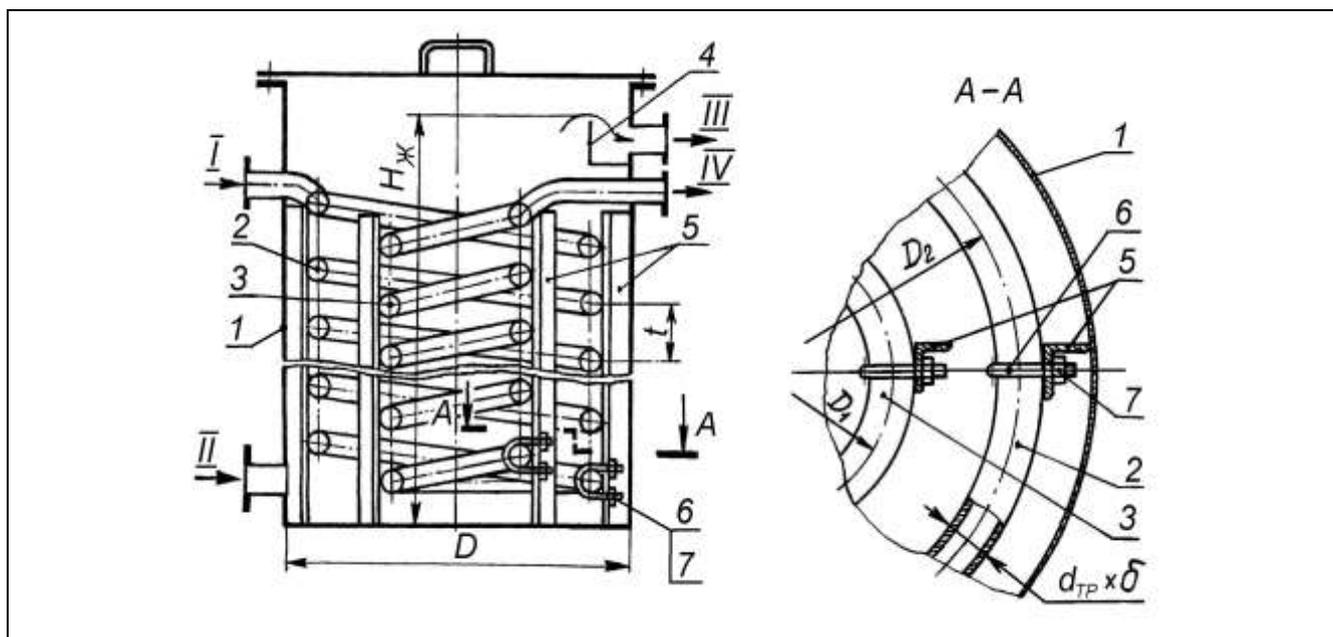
Погружной цилиндрический теплообменник с двумя соосными змеевиками: 1 – цилиндрический корпус; 2 – наружный змеевик; 3 – внутренний змеевик; 4 – переливной карман; 5 – стойки из уголков; 6 – хомут; 7 – гайка. Штуцера: I – вход охлаждаемого продукта; II – вход теплоносителя; III – выход теплоносителя; IV – выход охлажденного продукта
